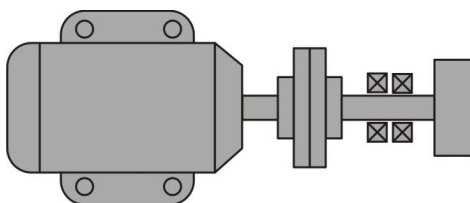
Схема контроля механических потерь на трение в подшипниках быстрогоходного вала шестерни
